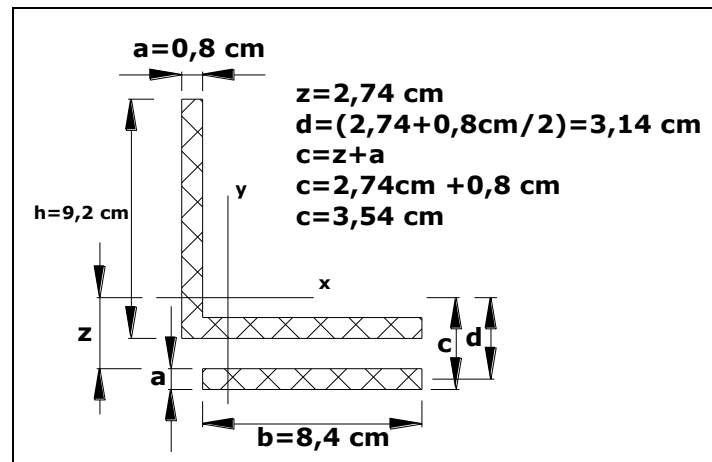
Parámetros para el cálculo de momento de inercia de soldadura.
